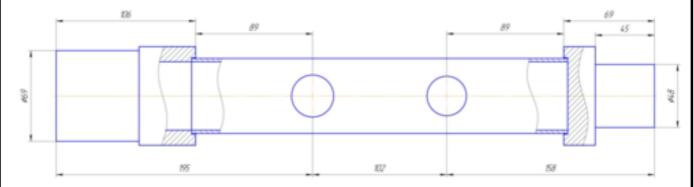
Схема сборки патрубка (поз. 1) с заглушкой и переходником Сборка фиксируется прихватками. После сборки производится сварка. Шов, соединяющий патрубок с заглушкой и патрубок с переходником является нестандартным. Общий вид шва показан на рисунке 2.9.
